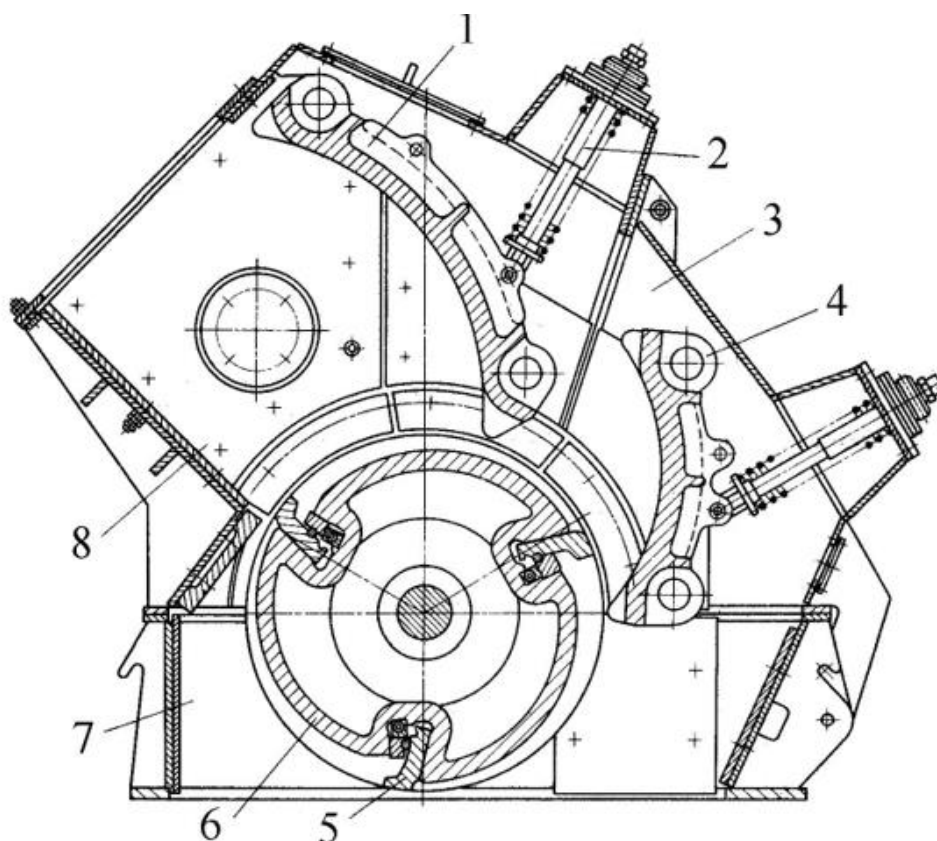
Однороторна дробарка крупного дроблення СМД-86А
